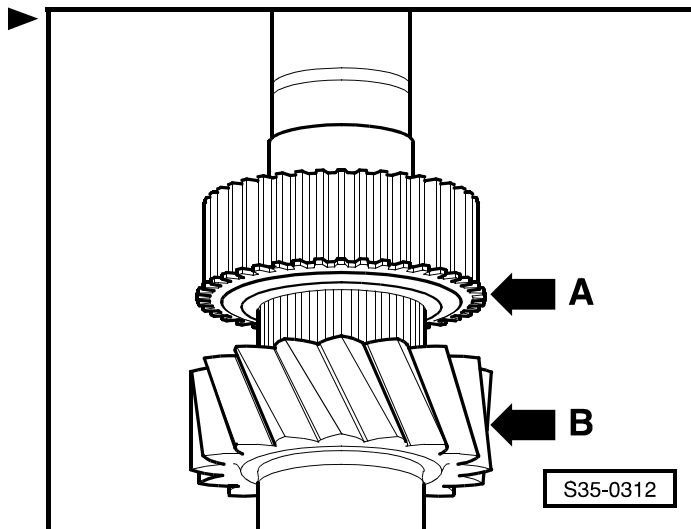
Запрессовывание каретки синхронизатора для передачи заднего хода
